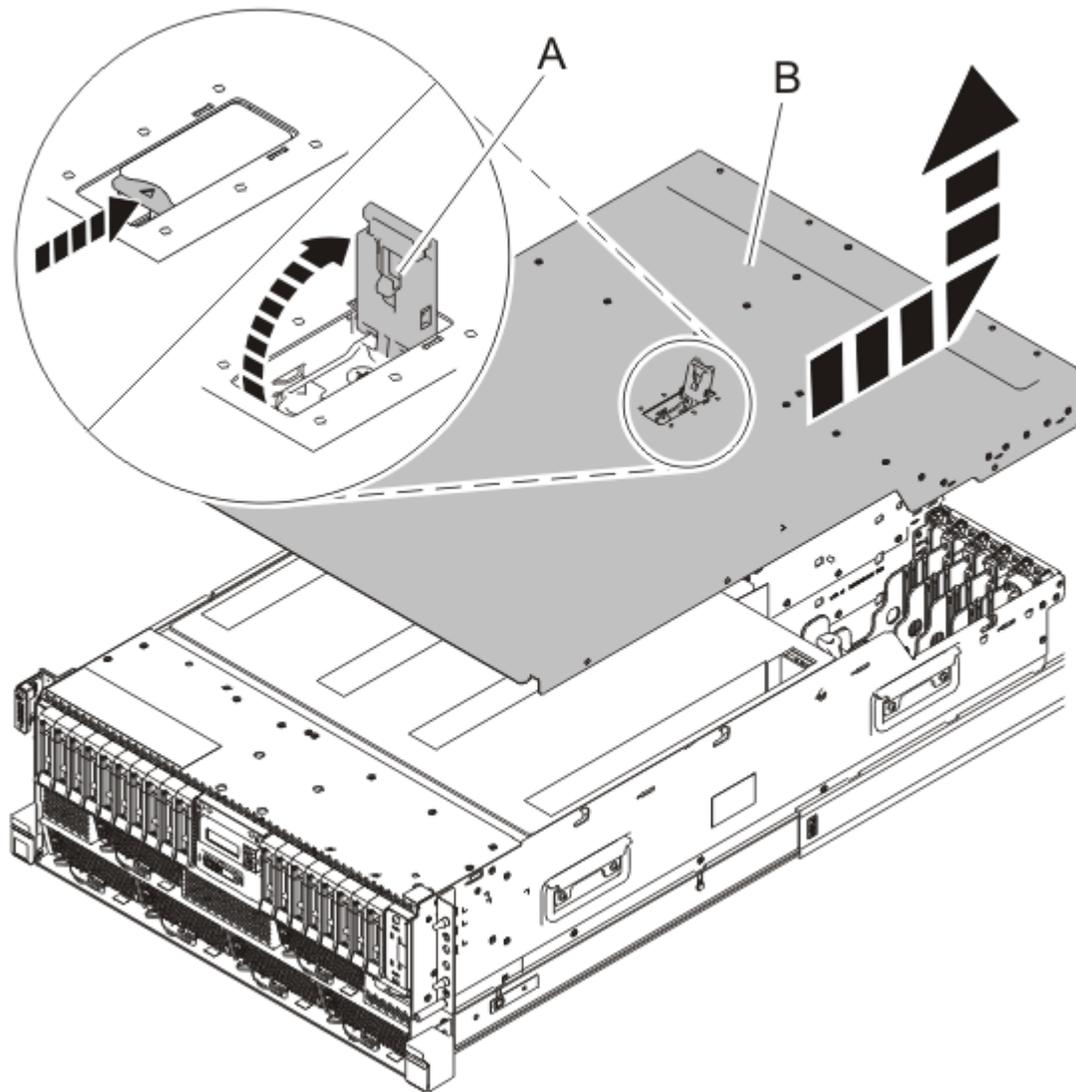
Removendo a Tampa de Acesso de Serviço de um Sistema Montado em Rack
